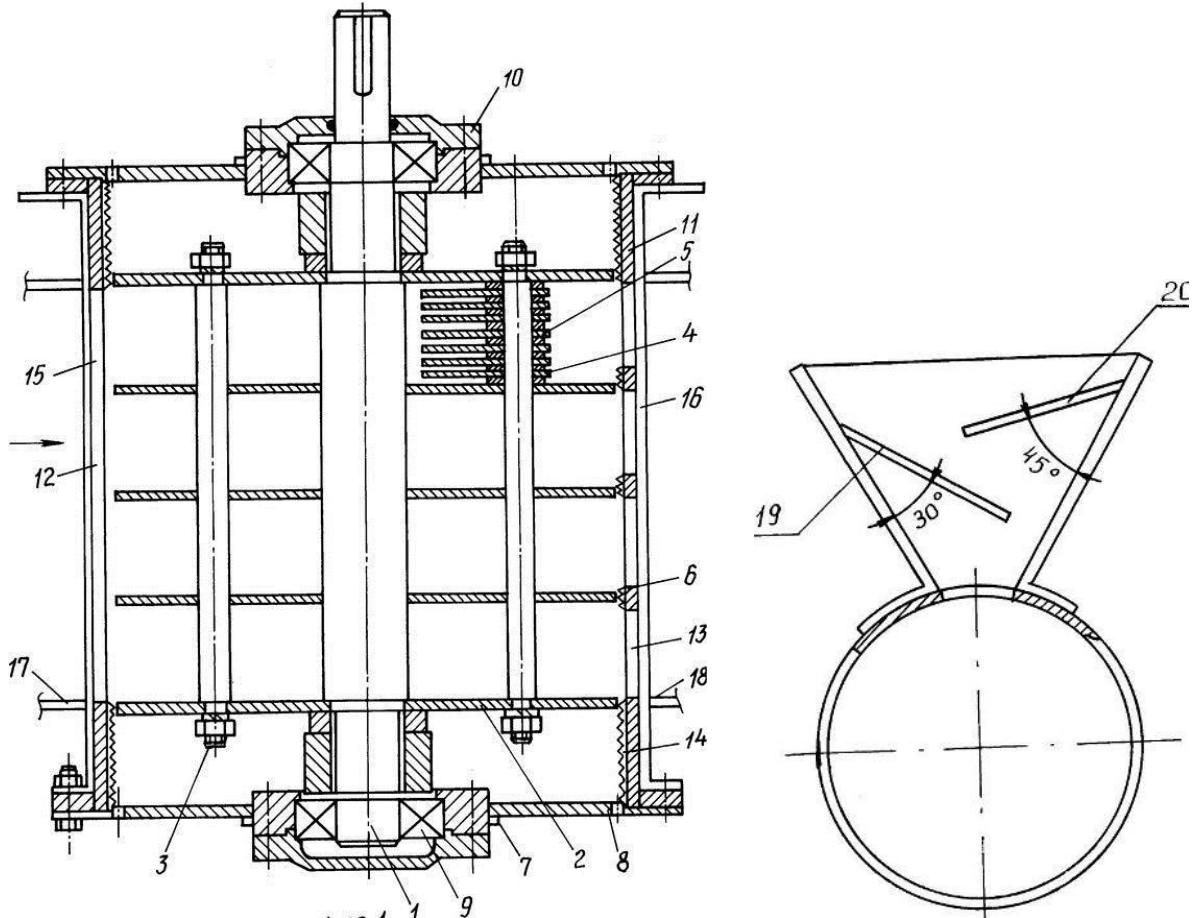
Молотковая дробилка Патент РФ 2106911
